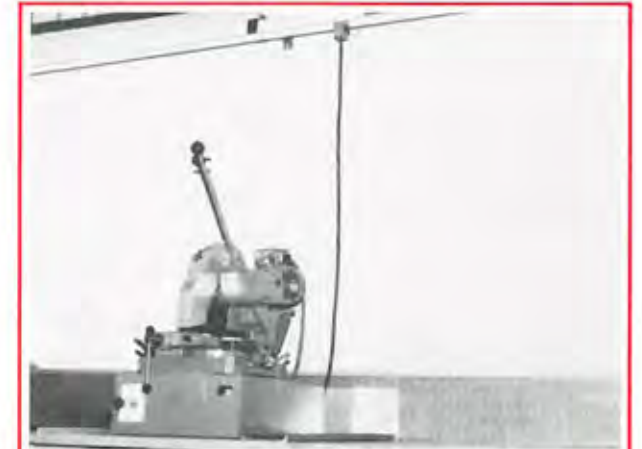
Anschluss einer kleinen Werkzeugmaschine durch Steckabnehmer.
